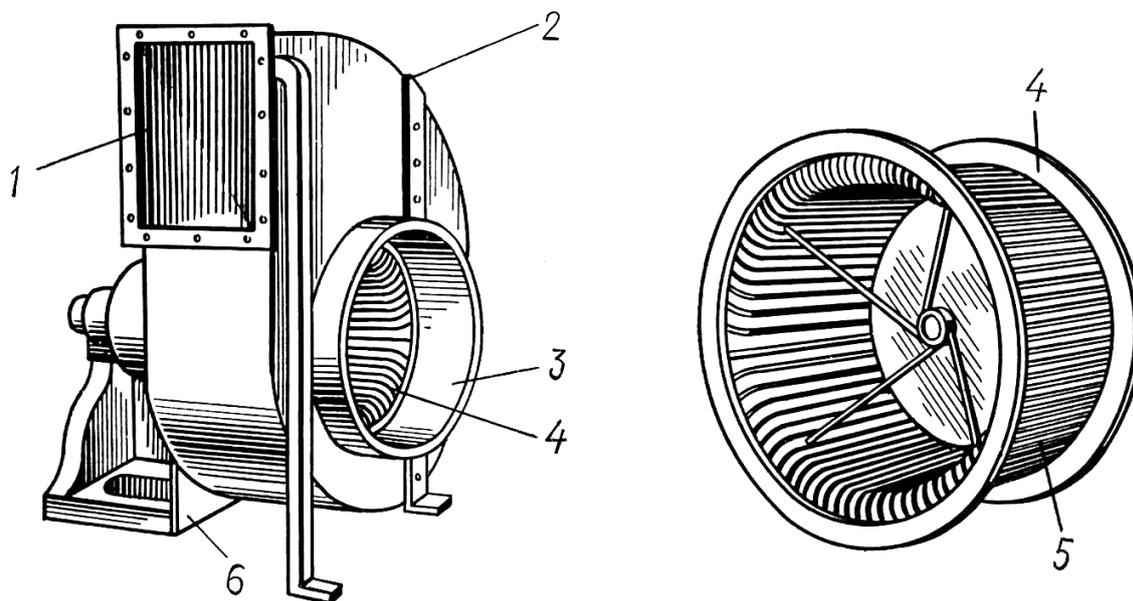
Вентилятор: 1 – нагнетательный патрубок; 2 – корпус; 3 – всасывающий патрубок; 4 – рабочее колесо; 5 – лопатки; 6 – станина
